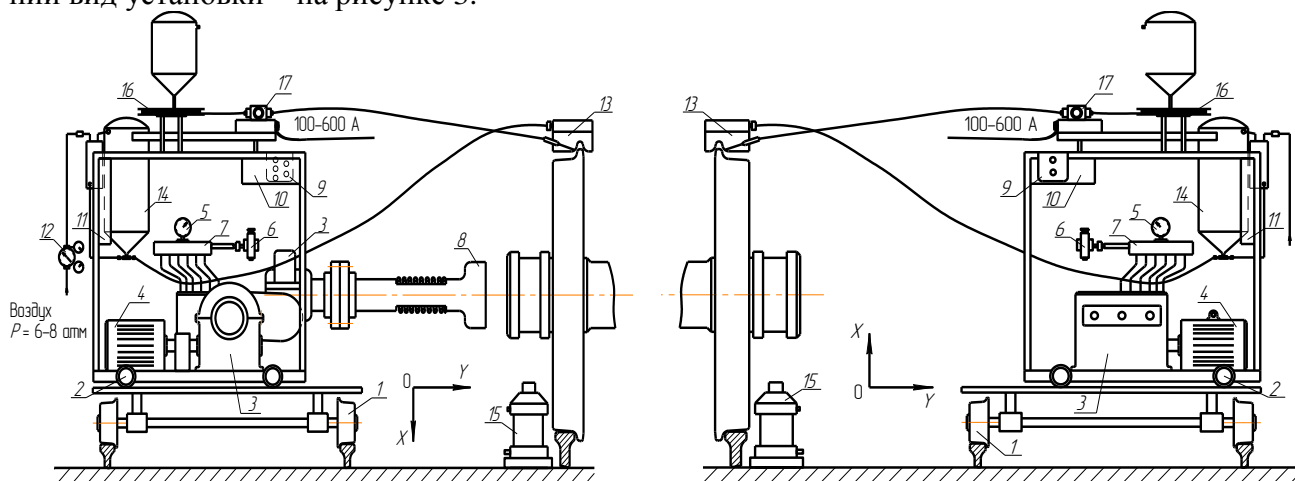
Схема установки для наплавки гребней бандажей без выкатки колесных пар из-под электровоза ПЭ2^М
